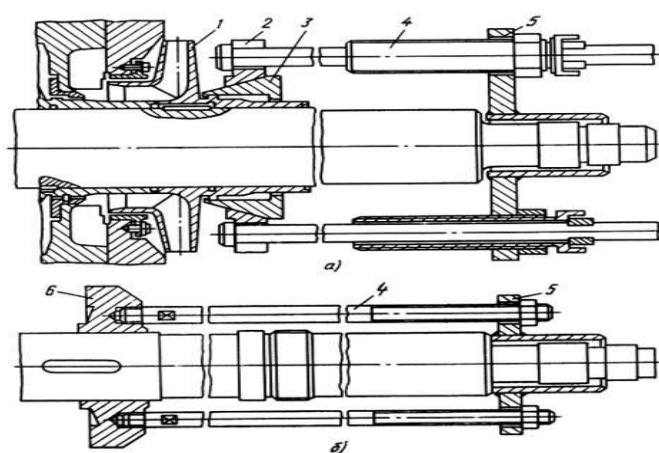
Приспособления для снятия деталей с вала насоса
